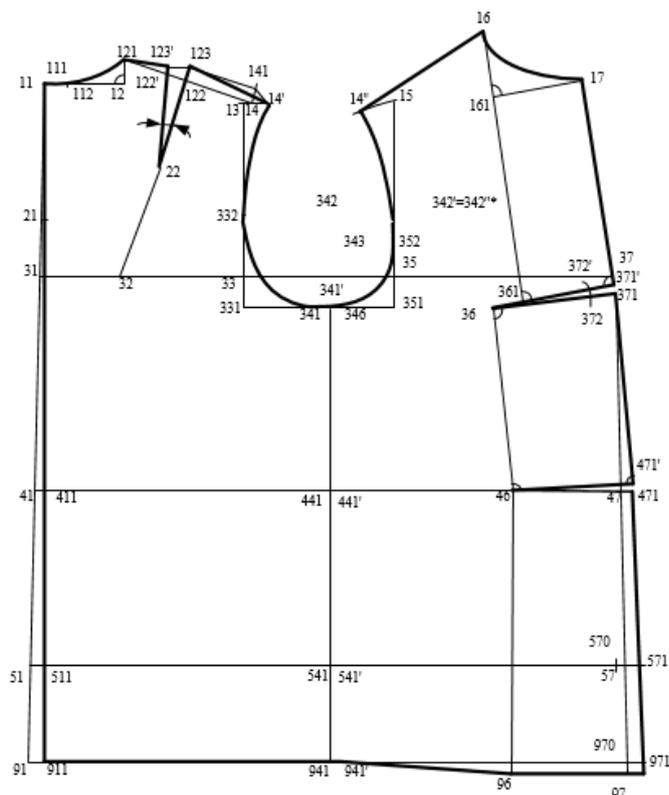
Чертеж базовой конструкции тактической разгрузки
